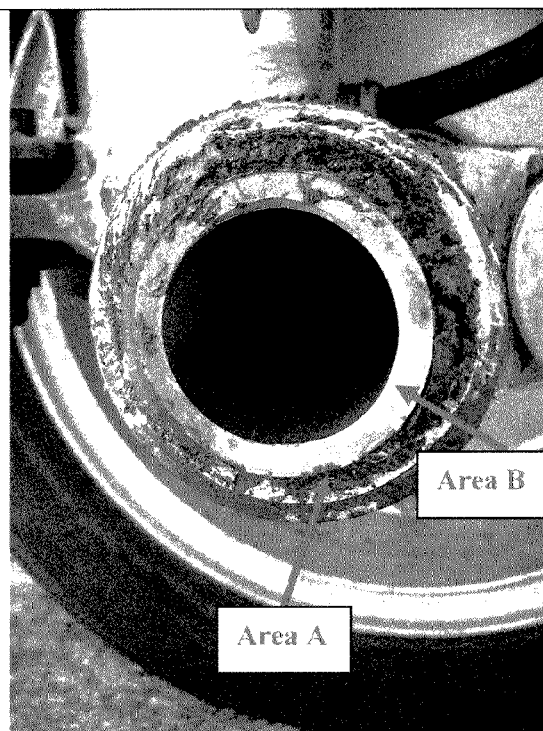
superficie di rottura dell'assale collegata all'inner cylinder, aree A e B.
